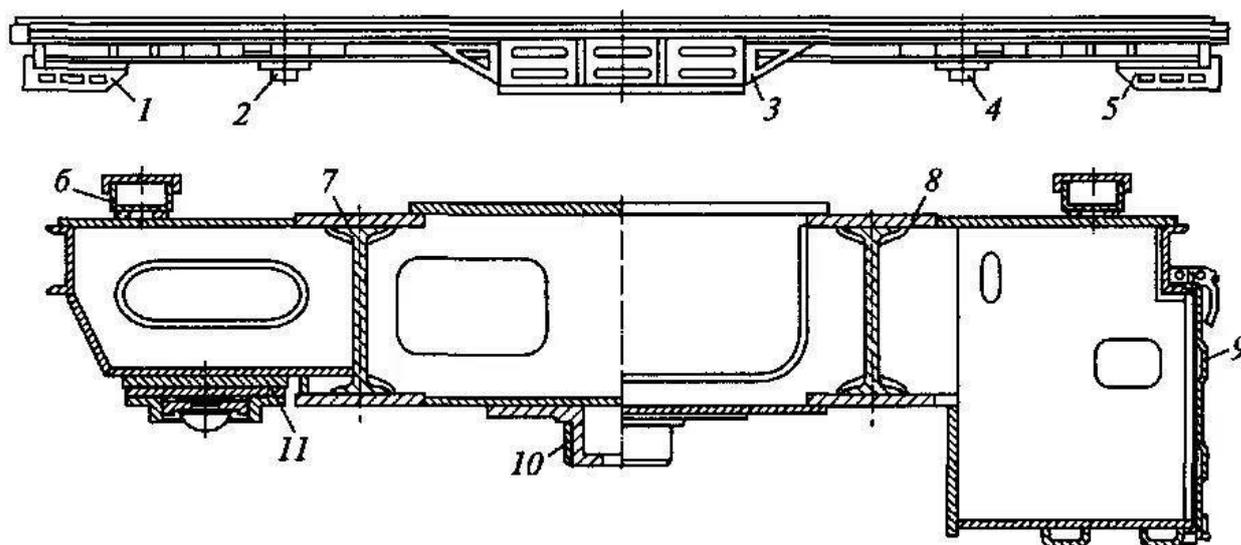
Главная рама тепловоза: 1, 5 - стяжные ящики; 2, 4 - шкворни; 3 - ферма, усиливающая главную раму; 6 - желоб с крышкой для кабеля; 7 - хребтовая балка; 8 - стальная полоса усиления балки; 9 - крышка шкафа аккумуляторной батареи; 10 - стальное кольцо шкворня; 11 - специальный лист для установки верхней части опорно-возвращающего устройства
